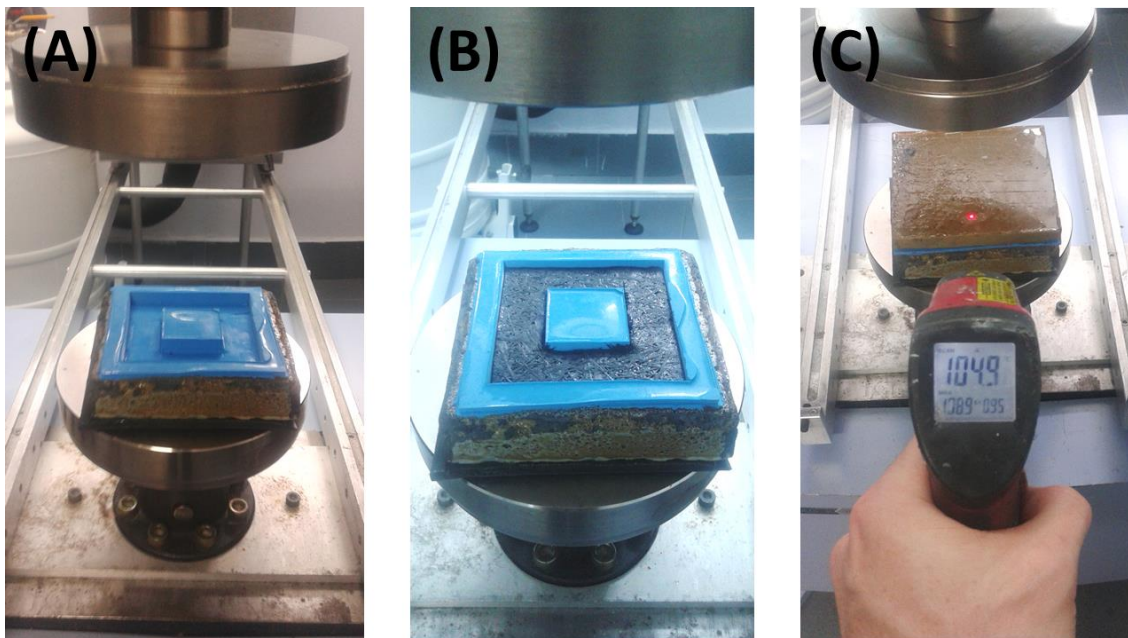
(A) Colocación del molde en la máquina de ensayos universales; (B) Introducción del preimpregnado; (C) Medición de la temperatura del molde previo al inicio de la compresión.
